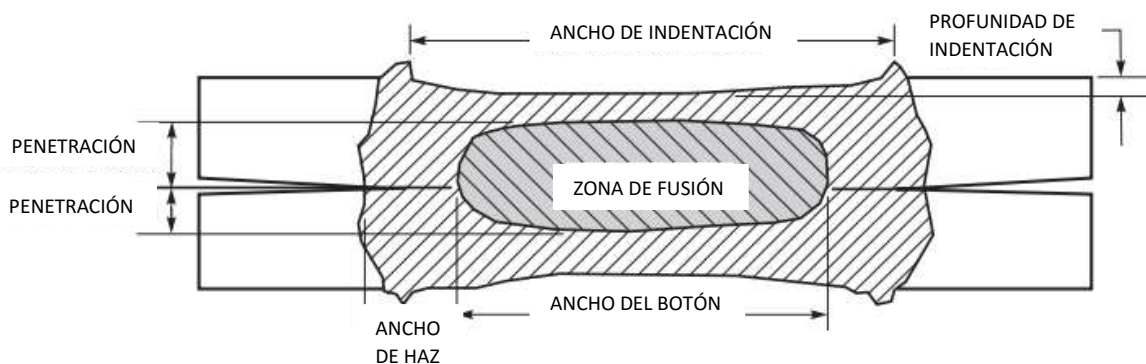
Sección transversal de una soldadura por puntos de resistencia [22].
